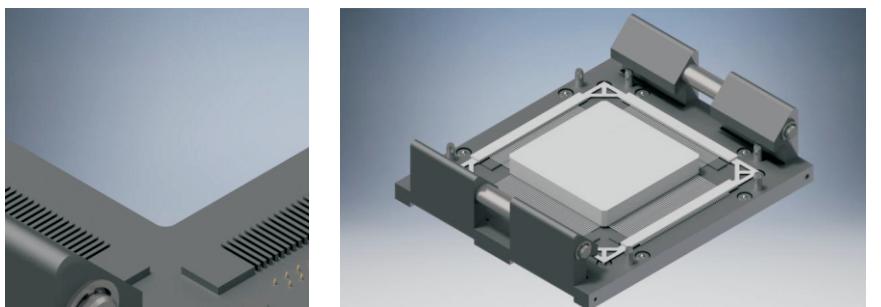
Внешний вид КУ для корпусов с керамической рамкой
